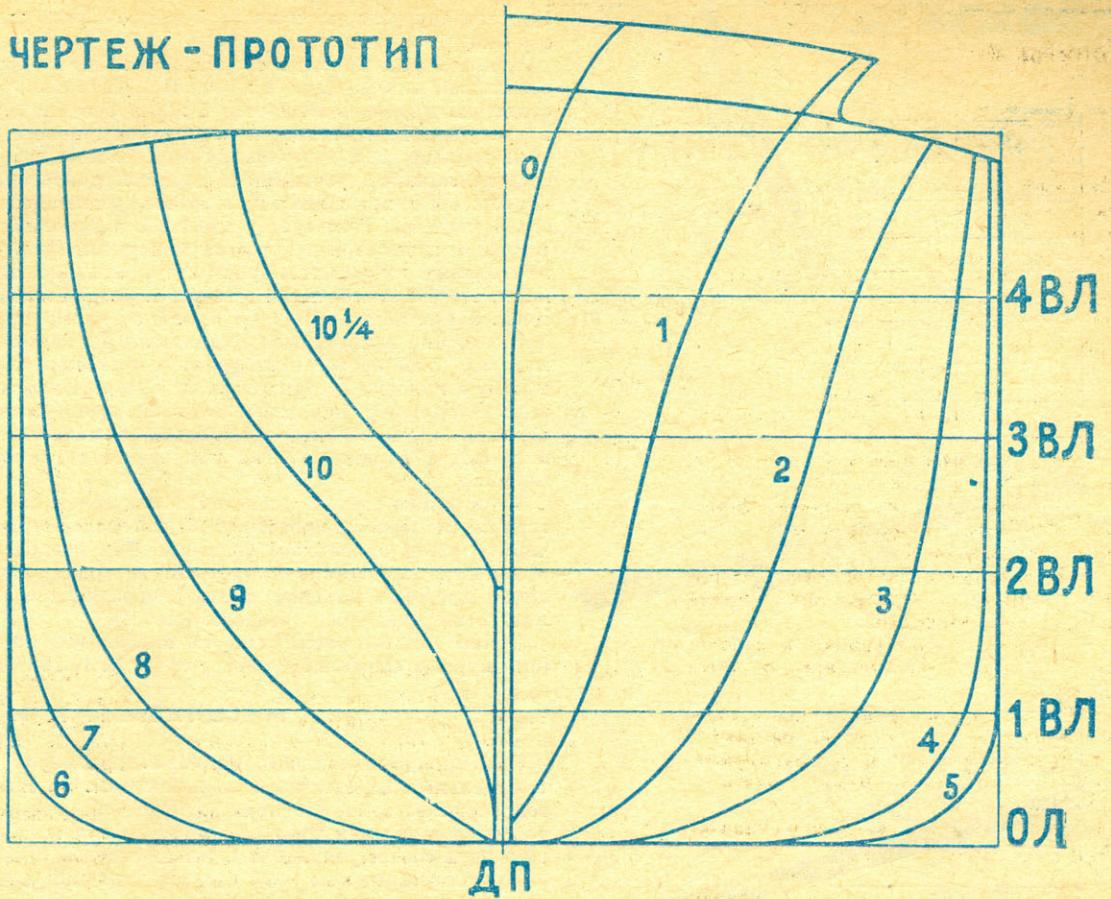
Теоретический чертеж корпуса, который нужно уменьшить в 2 раза.
